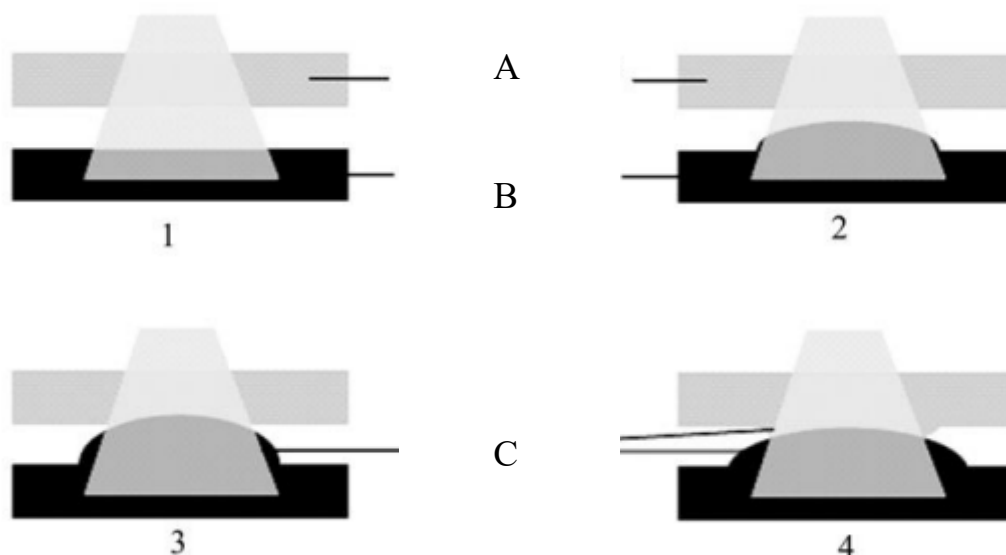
Схема лазерного зварювання полімерних матеріалів:
